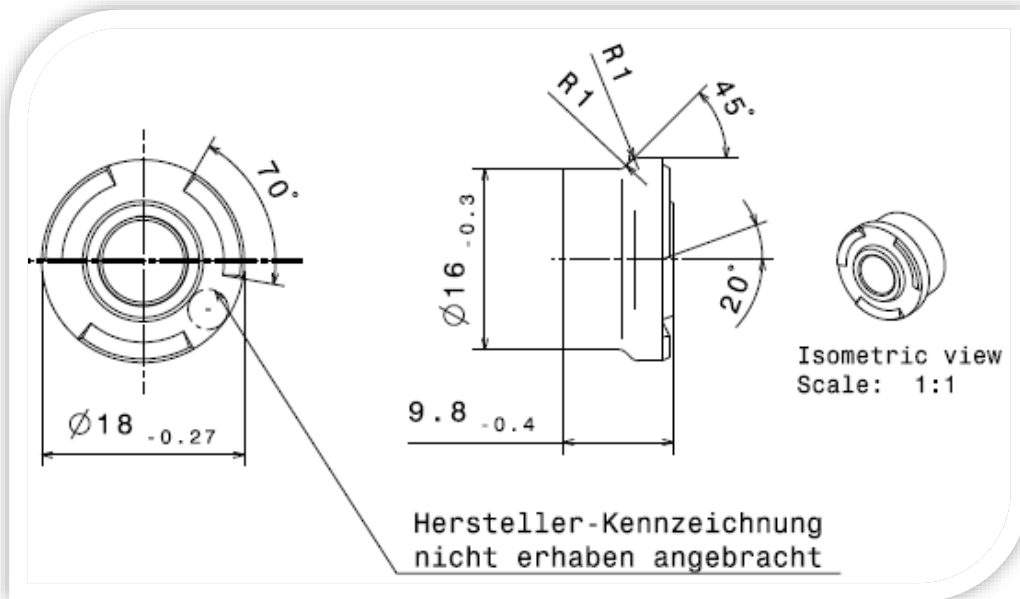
Auszug aus der Zeichnung der geschweißten Mutter.
